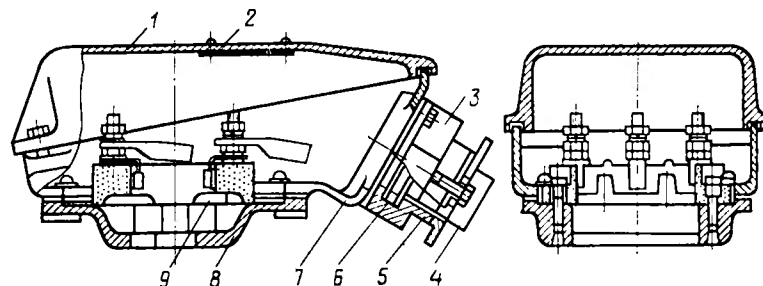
Выводное устройство для двигателей с $H=160...250$ мм: 1 — крышка, 2 — табличка-схема, 3 — гнездо, 4 — втулка, 5 — уплотнительная втулка, 6 — уплотнительное кольцо, 7 — корпус, 8 — патрубок, 9 — панель с контактными болтами
